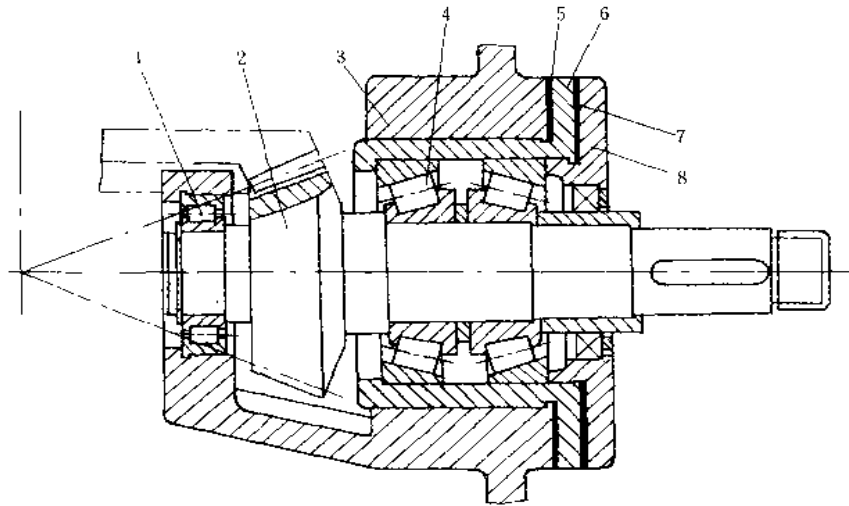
小圆锥齿轮轴轴承间隙和齿轮啮合调整
